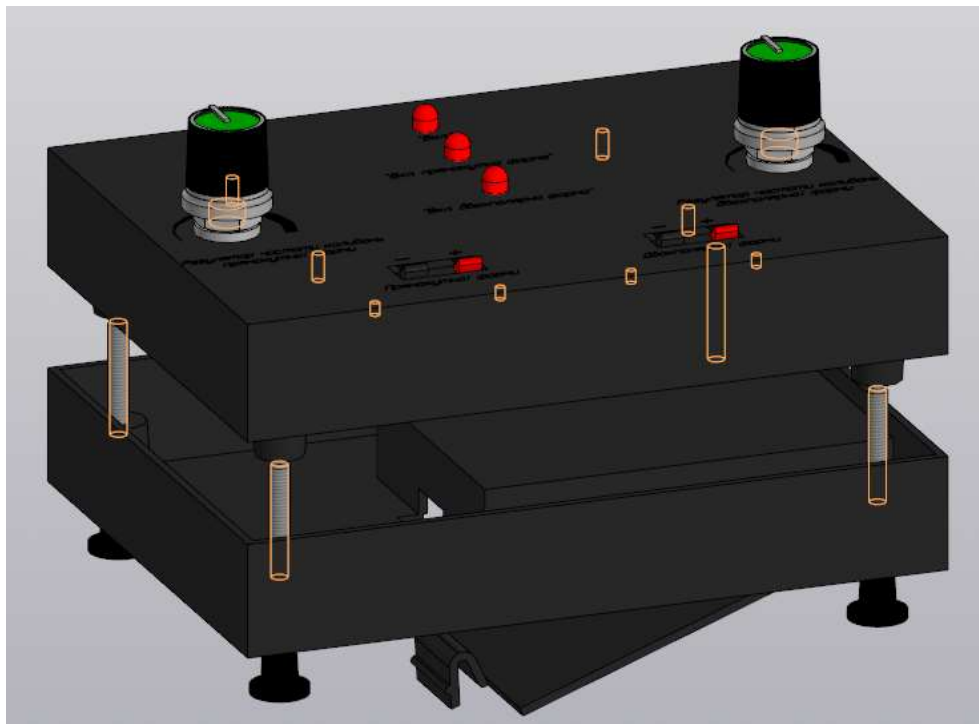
3D модель пристрою, загальний вигляд
